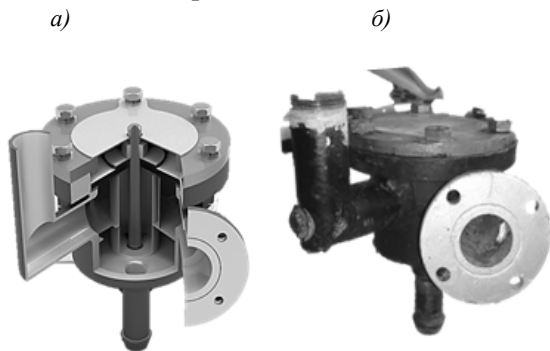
Розріз моделі лабораторного зразка: 1 – корпус; 2 – вхідний патрубок; 3 – вихідний патрубок очищеного повітря; 4 – стакан; 5 – конденсаційний жолоб; 6 – додатковий зливний отвір для вологи; 7 – зазор; 8 – торцева стінка; 9 – основний зливний отвір «вікно»; 10 – зливна труба для вологи; 11 – упор для монтажу конструкції на стенді
